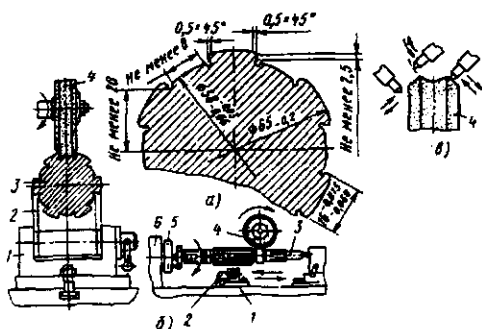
Схема шлифования дна и боковых поверхностей шлицев профилированным кругом: а – конфигурация и размеры обрабатываемой шлицевой поверхности вала; б – схема наладки; в – схема профилирования круга
